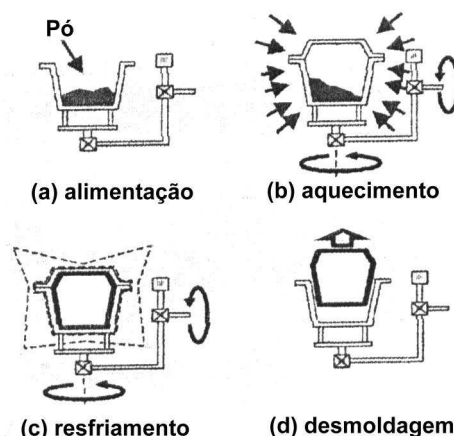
Diagrama esquemático do processo de moldagem rotacional [2].
